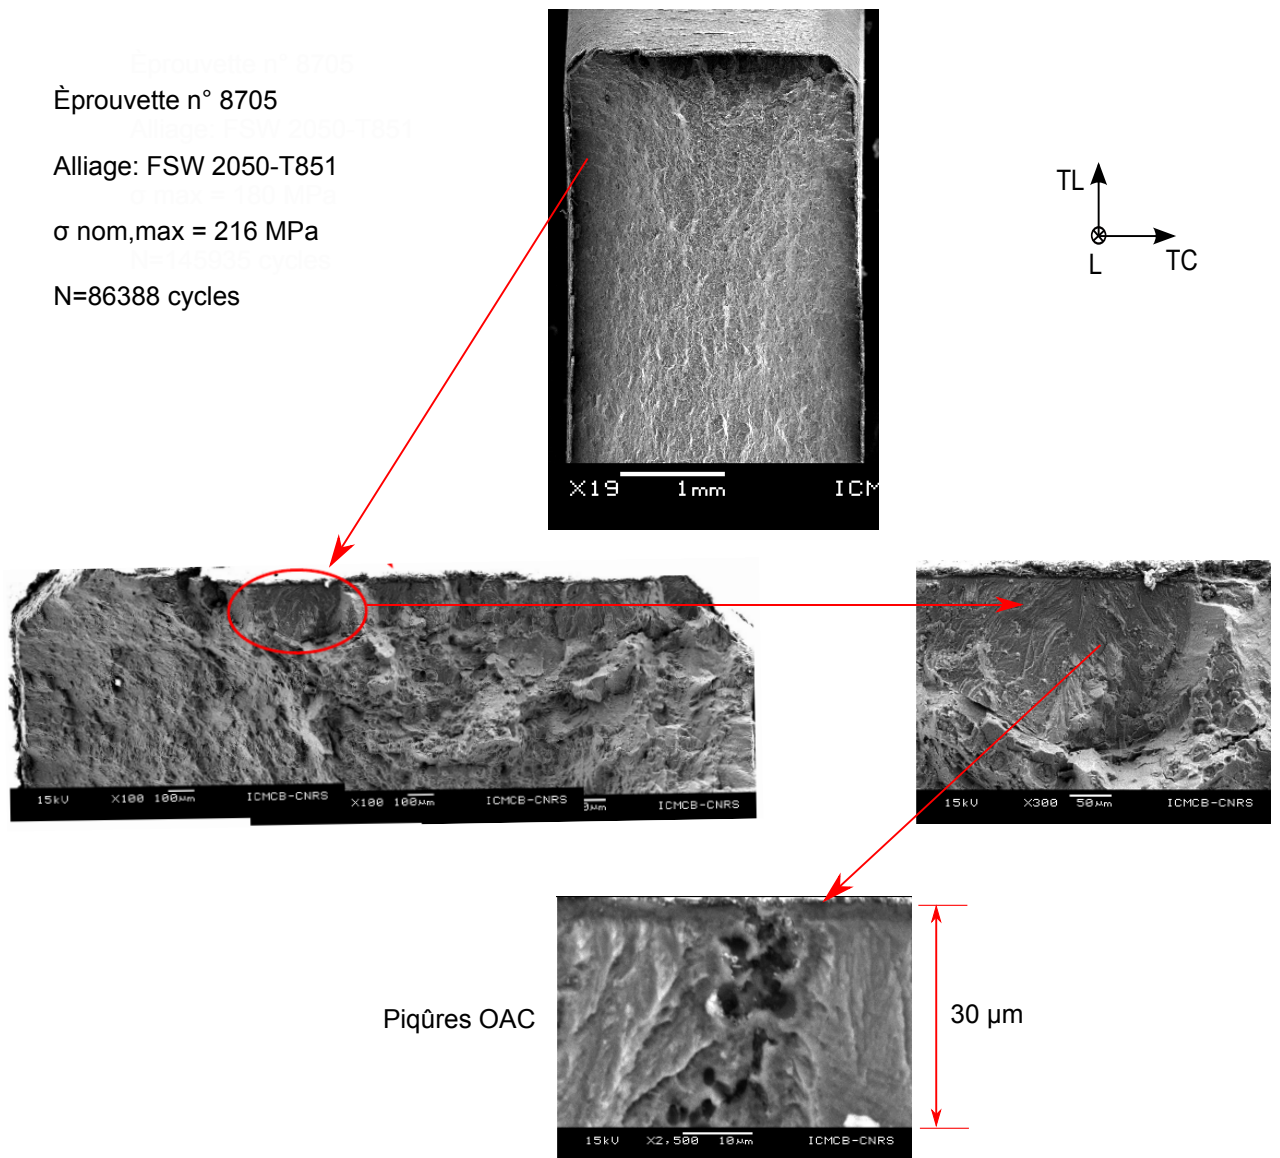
Fractographie d'un faciès de rupture d'une éprouvette T10 prélevée dans le sens L du joint soudé en alliage 2050-T851
